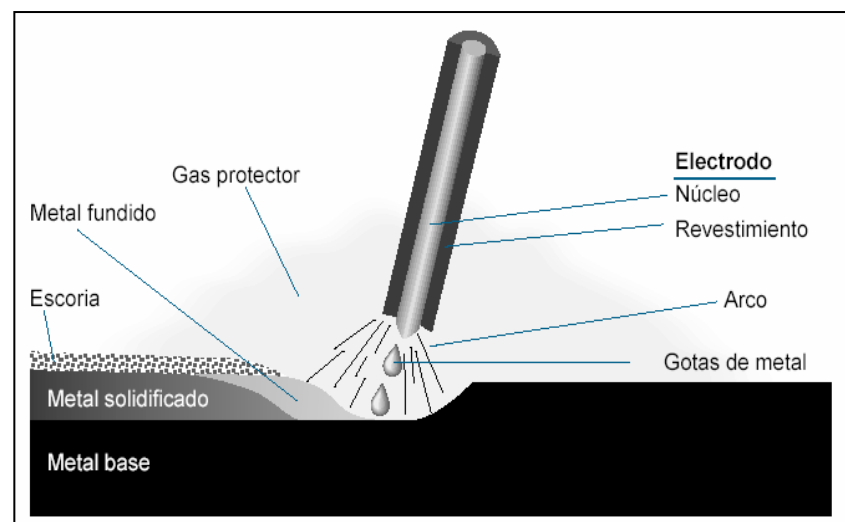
PROCESO DE SOLDADURA SMAW.
